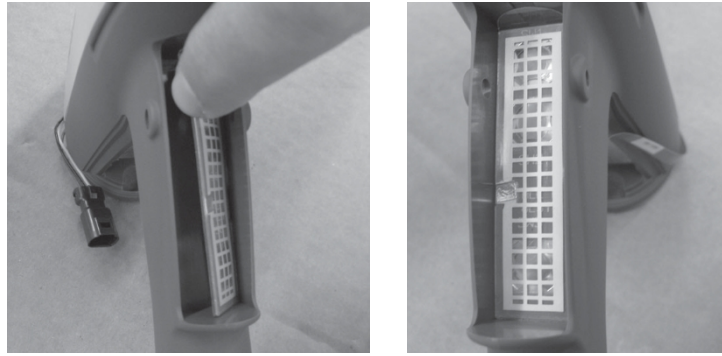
Installazione dell' Il'interruttore a grilletto - Fase 4
